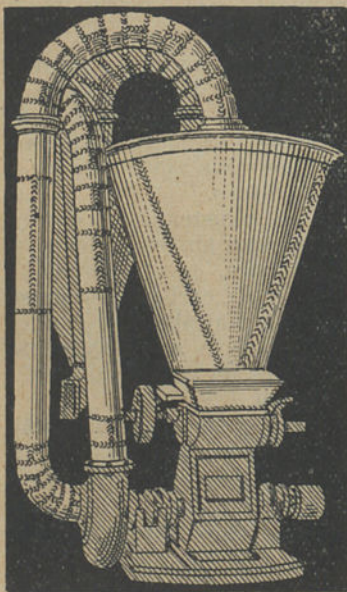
Construção de tubagens de grandes ventiladores pela soldadura autogenea.
